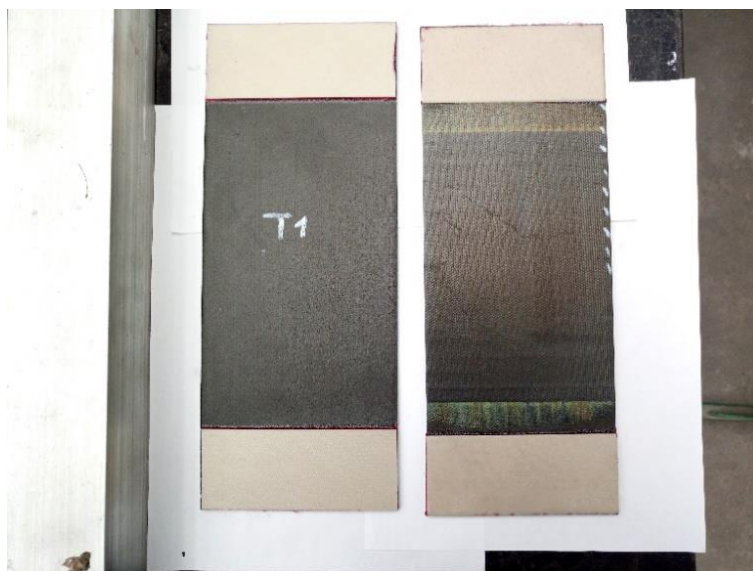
Paneles tipo 3 para las probetas de tracción
